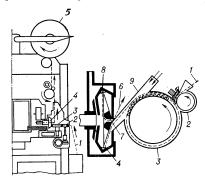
Схема пневмомеханической прядильной машины: 1 - лента; 2 - питающий цилиндр; 3 - дискретизирующий, или расчесывающий, валик; 4—прядиль-ная камера; 5— бобина; 6— пряжа; 7— направляющая трубка; 8— жёлоб; 9 — канал.
